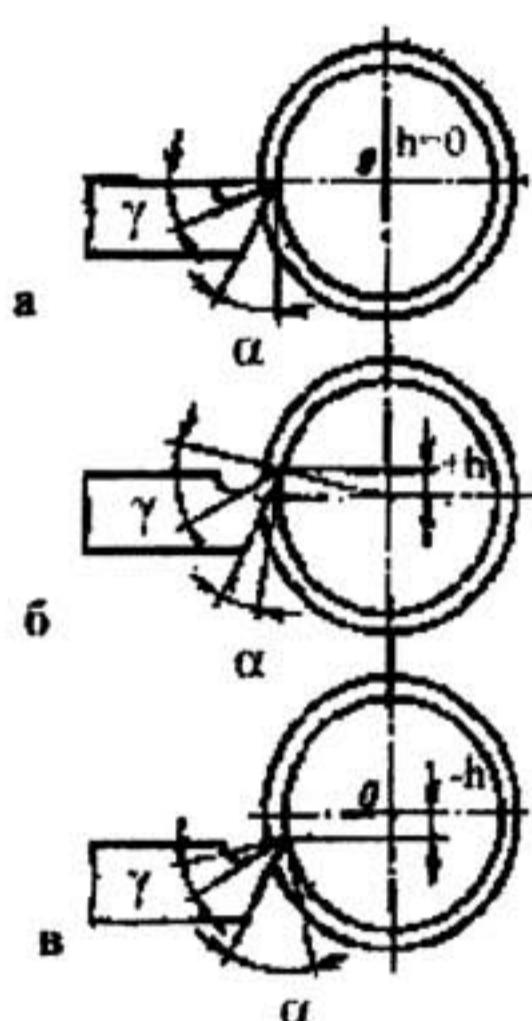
Углы α и γ при установке вершины проходного резцы относительно оси заготовки:
